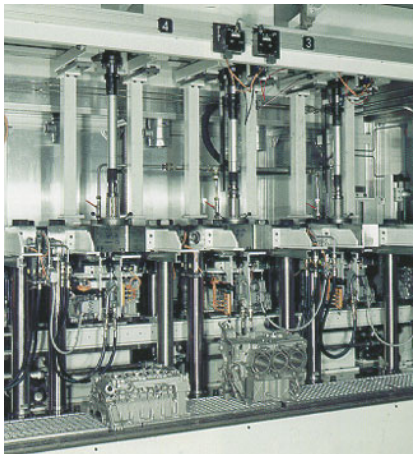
reZ) Transfer-Honmaschine für Zylindermotoren (Nagel)
